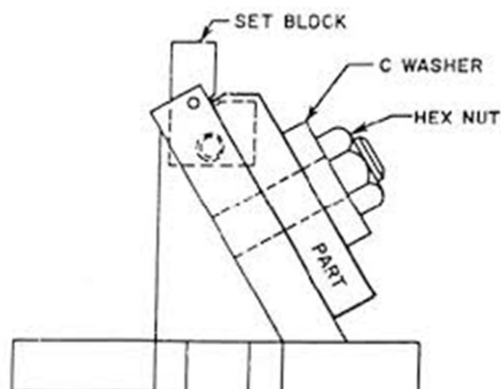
Fixture Sudut-Plat (Angle-Plate Fixture)
